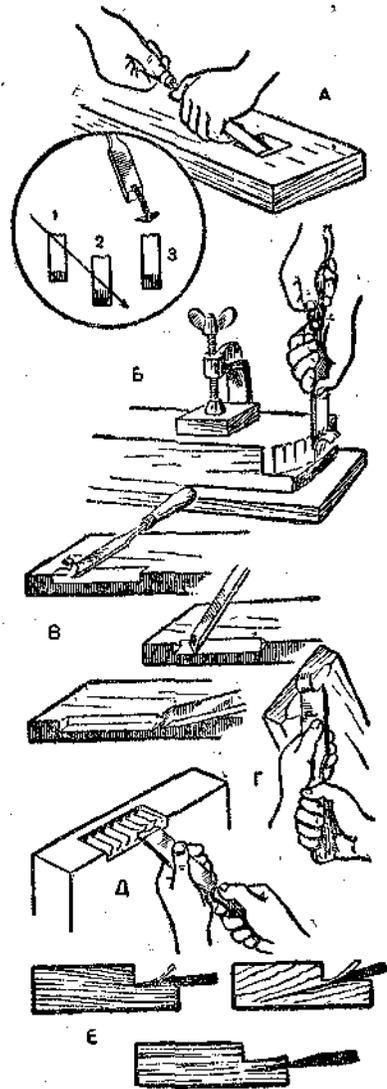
Последовательность операций при долблении: А — разметка заготовки рейсмусом; В — просечка контура гнезда; В — процесс долбления гнезда.
